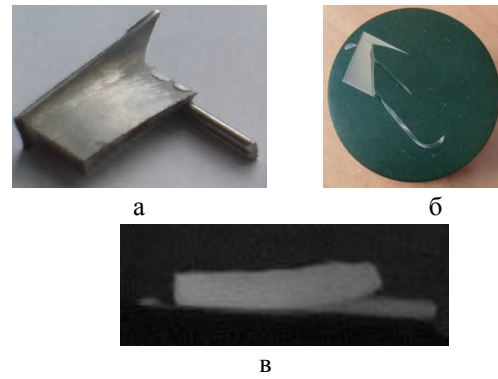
Общий вид образцов из лопатки КВД (а) и металлографического шлифа (б), рентгеновский снимок образца для исследования поверхностного слоя (в)
